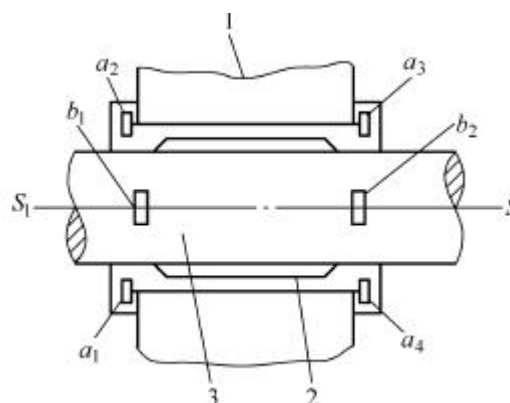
压铅法测量轴承顶间隙 1-轴承座；2-轴瓦；3-轴
